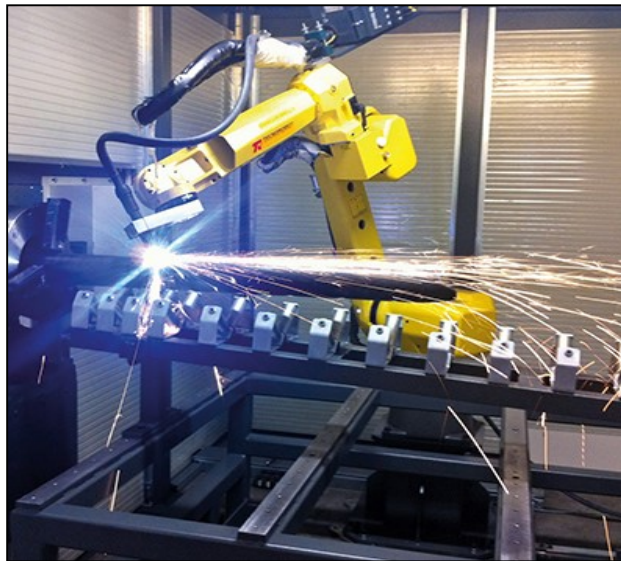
Soldadura ponto por ponto com um maçarico de solda
